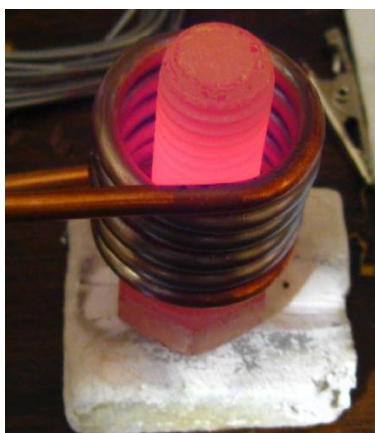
Calentamiento por acoplamiento sin contacto [2.13].
